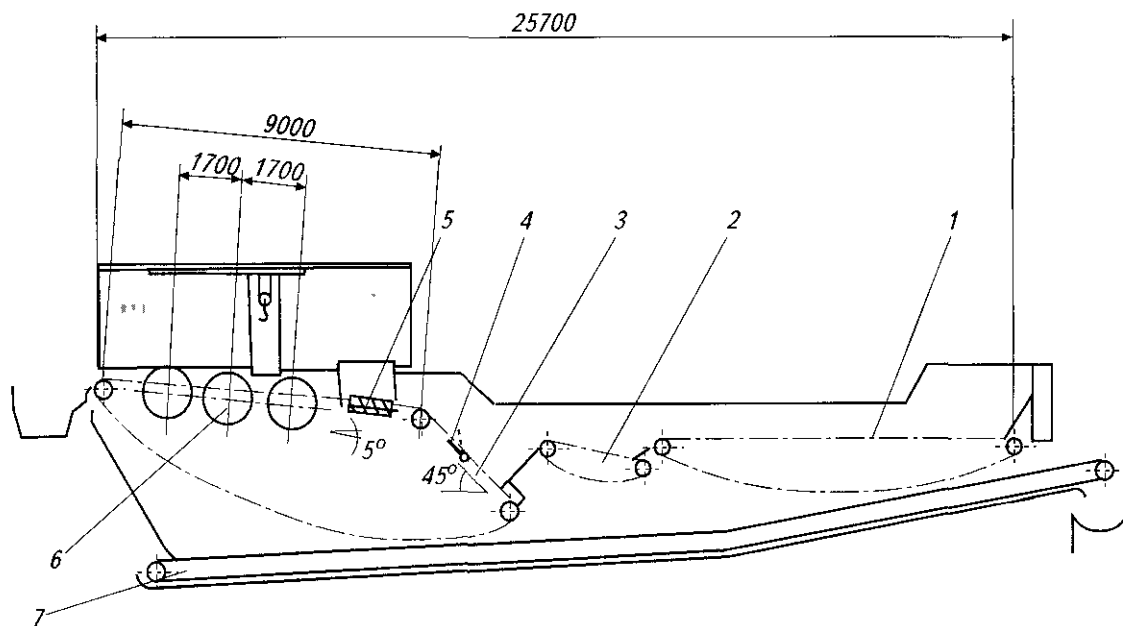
Агрегат слешерного типа «Комби-10» для приема и распиловки бревен:
